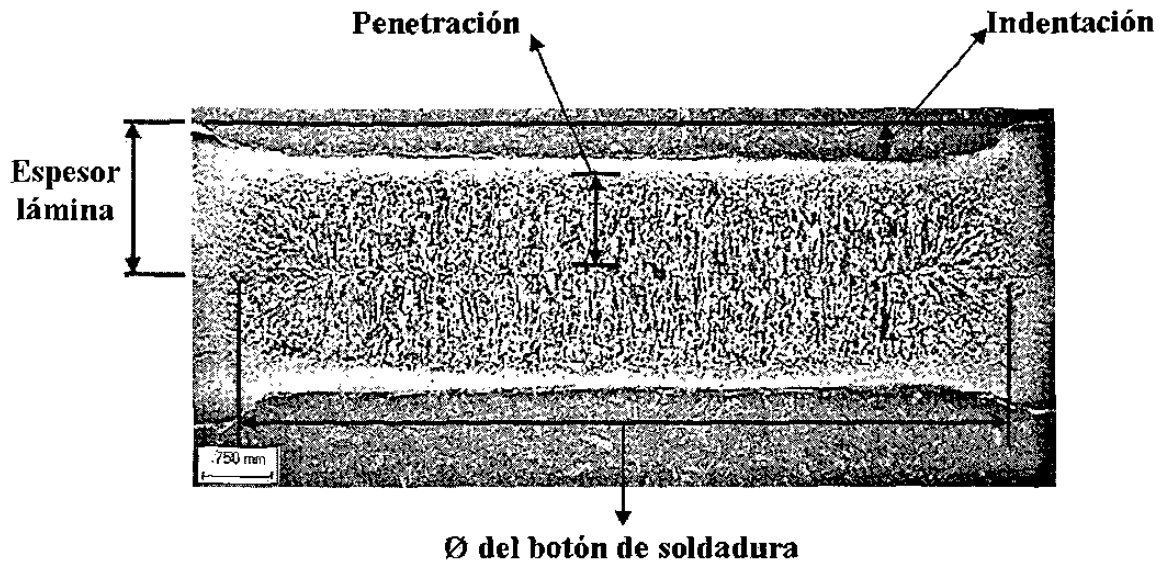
Parámetros dimensionales del botón de soldadura.
